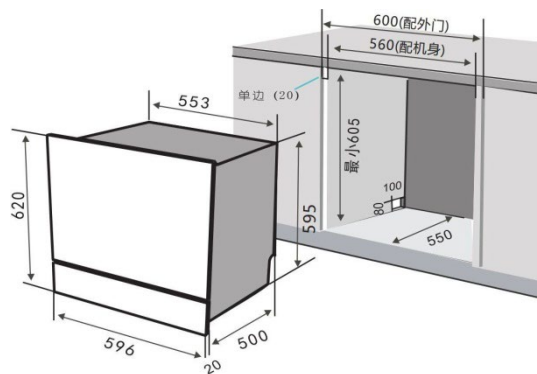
Габаритные размеры изделия и размеры ниши для установки
